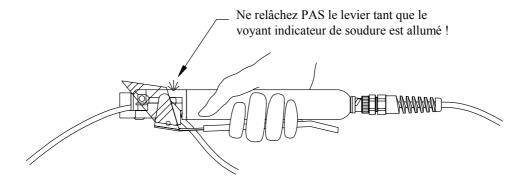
Maintien de la compression pendant la totalité du processus de soudure
